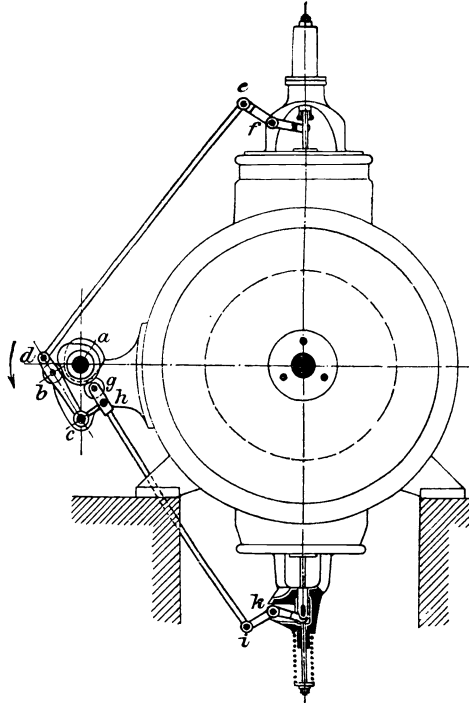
Steuerung mit unrunderen Scheiben am Niederdruckzylinder einer liegenden Dampfmaschine von Gebr. Sulzer. Die Vorrichtungen zum Verstellen der Stangenlänge sind weggelassen.
